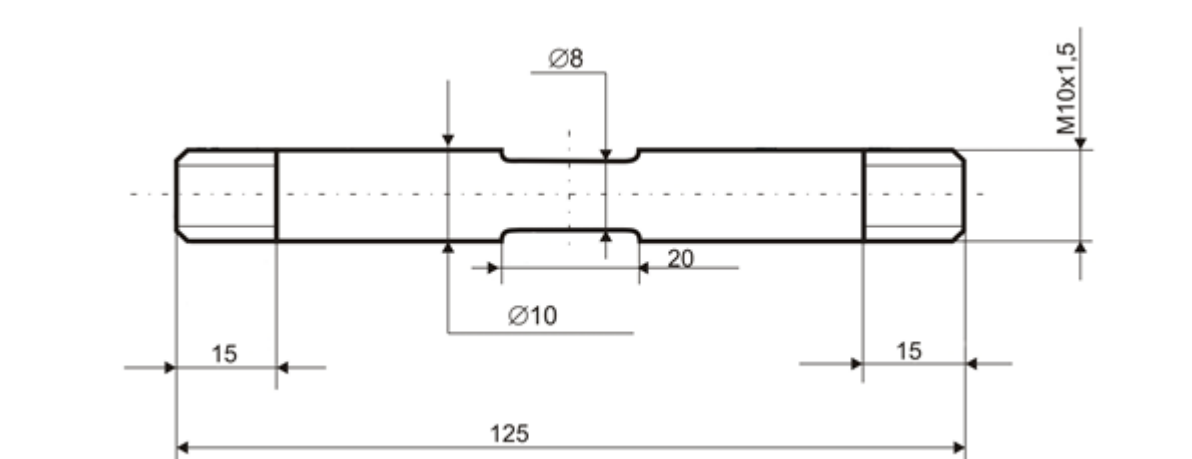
Эскиз образца для испытаний на установке Gleeble 3800
